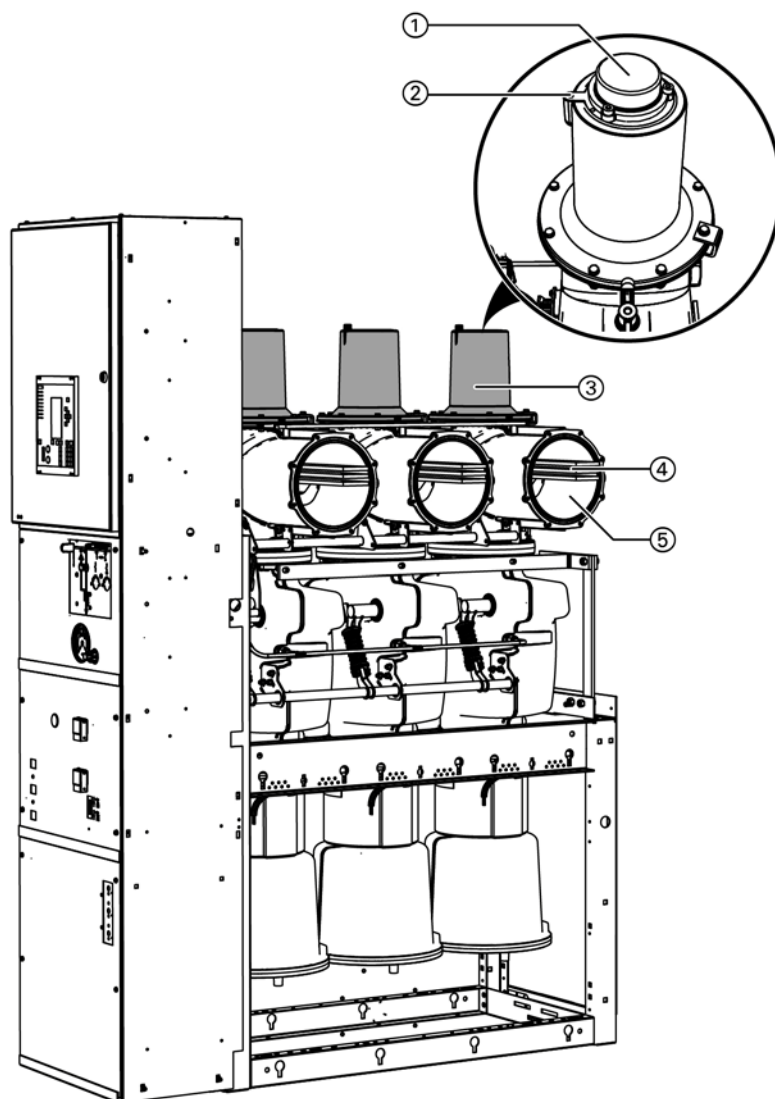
Обзор компоновки сборных шин: емкостный отвод напряжения
